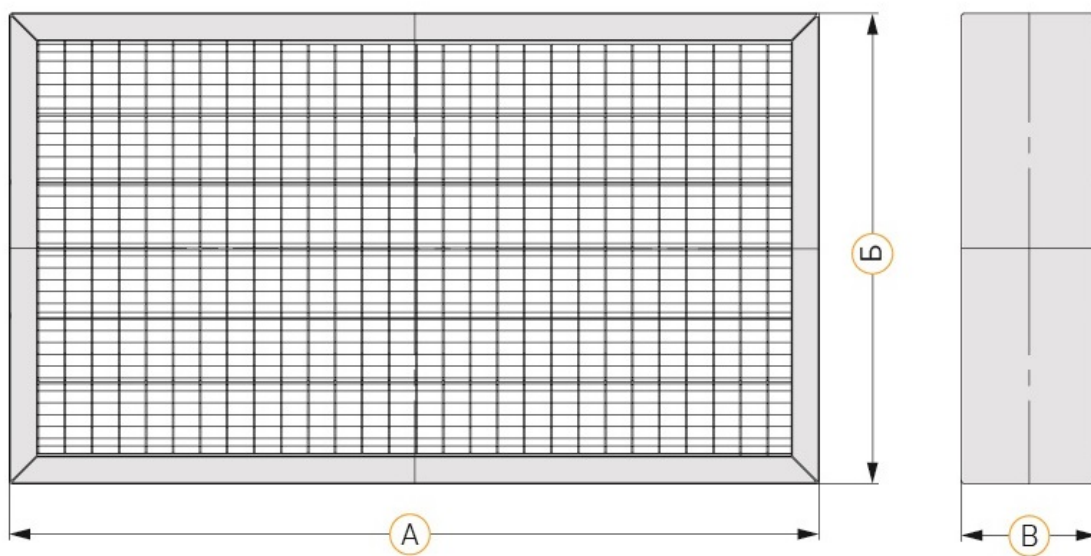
Внешний вид и основные размеры фильтрующих вставок SPR
